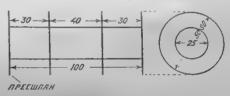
Формы и размеры каркаса для намотки катушки трансформатора для выпрямителя.
